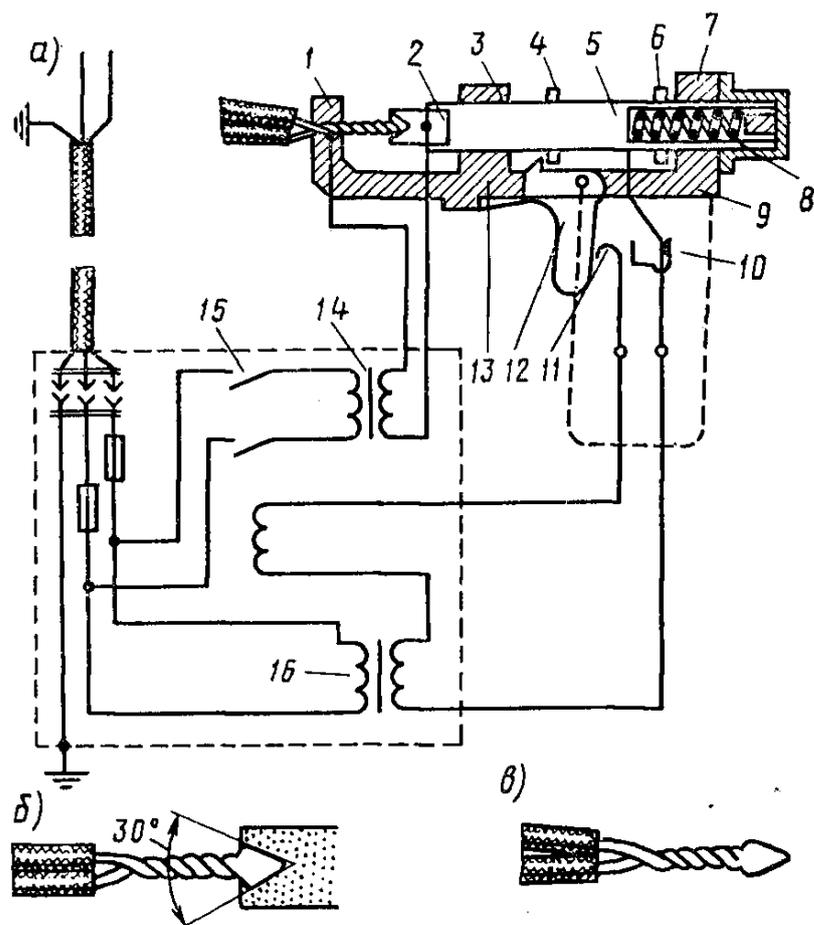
Сварка алюминиевых жил аппаратом ВКЗ-1: *а* - схема питания аппарата ВКЗ-1 при сварке; *б* - положение жил и электрода при сварке; *в* - готовое соединение; 1 - губки зажима проводов; 2 - угольный электрод диаметром 10 мм; 3 - передняя стойка с отверстием; 4 - передний бортик стержня; 5 - полый стержень подачи; 6 - задний бортик стержня; 7 - задняя стойка с отверстием; 8 - пружина подачи; 9 - сварочный пистолет; 10 - контакт отключения; 11 - контакт включения; 12 - спусковой рычаг; 13 - основание; 14 - трансформатор сварочный 220/10 В; 15 - реле включения; 16 - трансформатор управления 220/36 В
